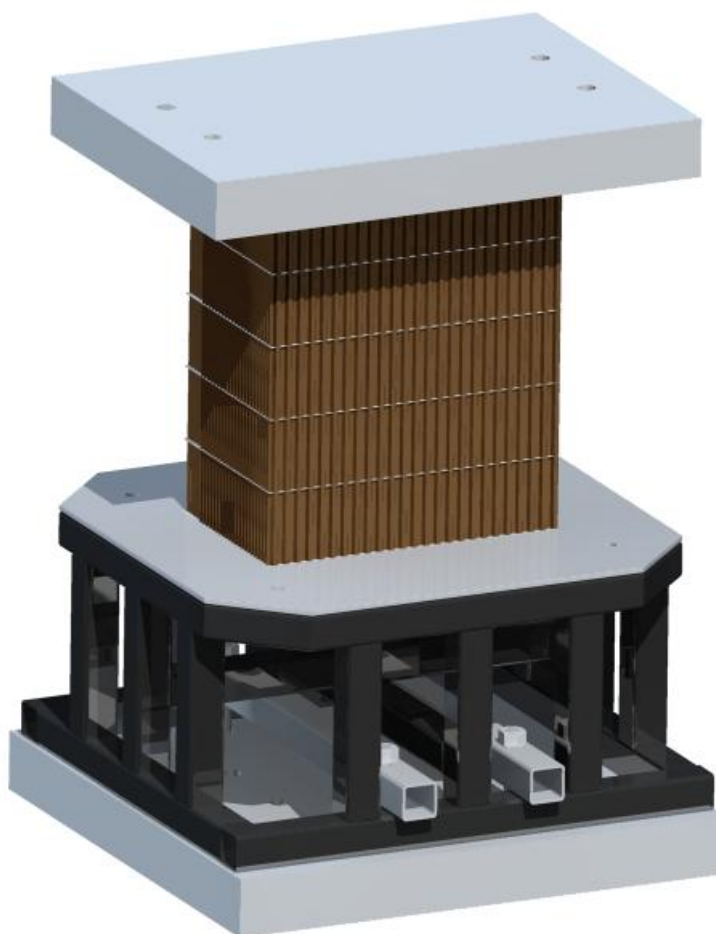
Model přípravku (Pro/ENGINEER)
